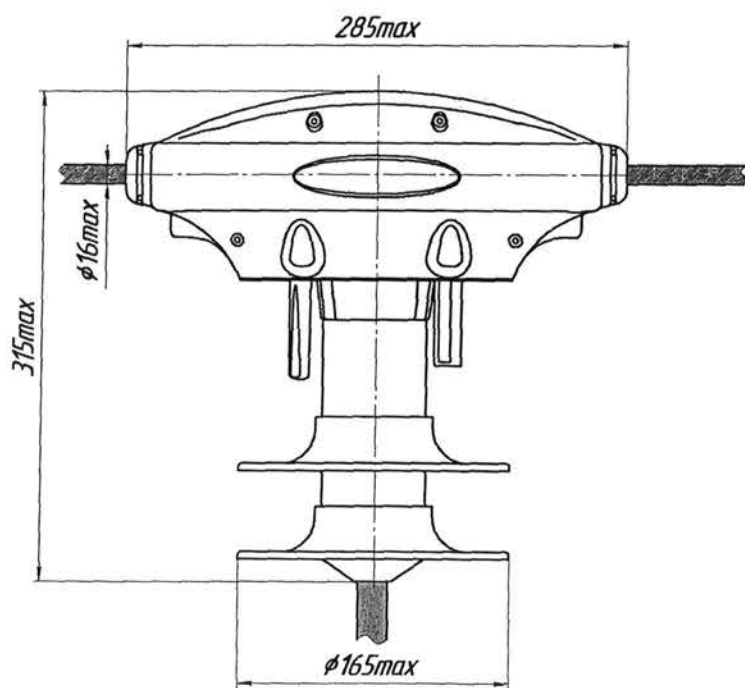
Габаритные, установочные размеры ДИЭ
